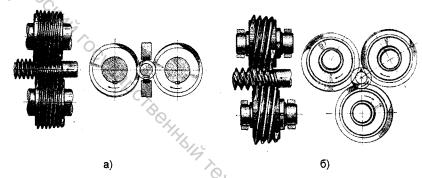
Схемы накатки резьб: а - двухвалковая; б - трехвалковая
